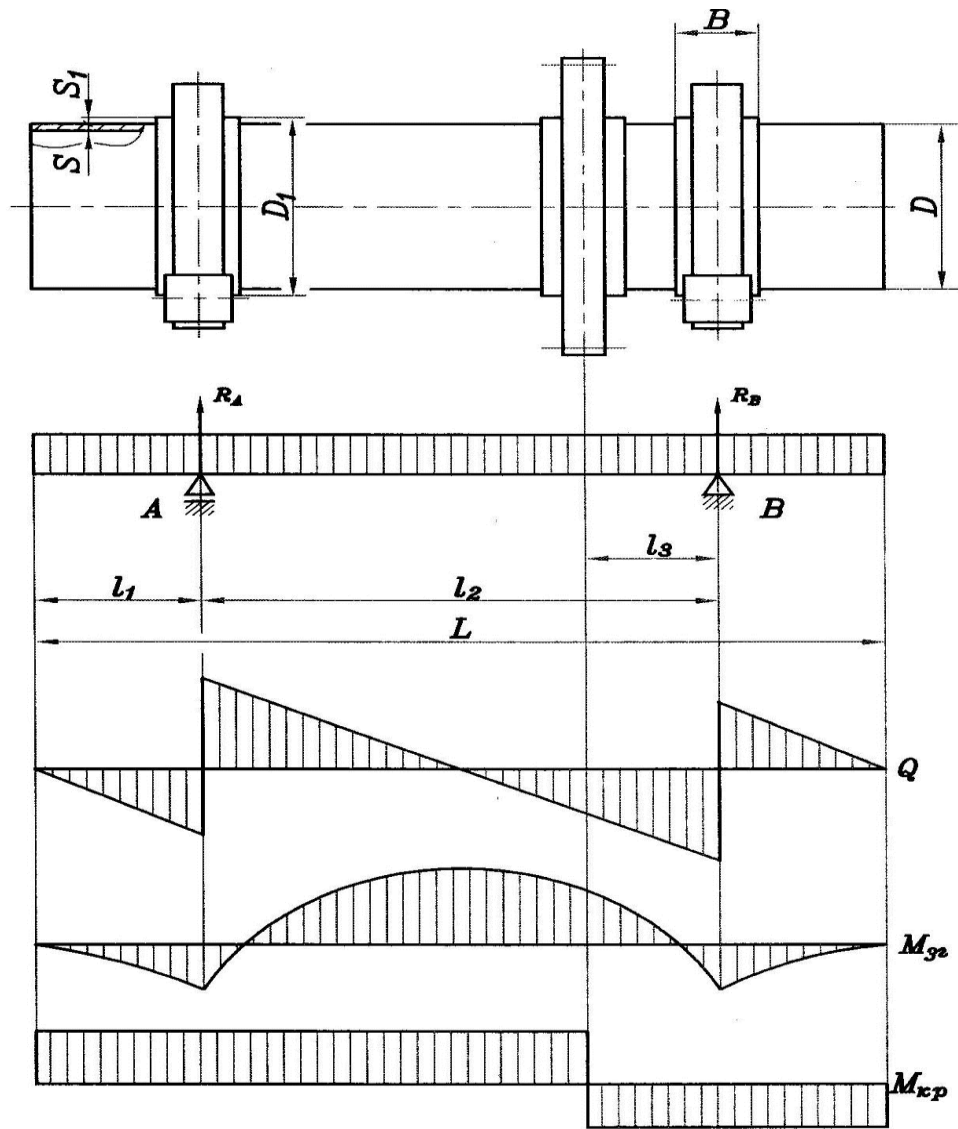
Розрахункова схема корпусу барабанної сушарки
